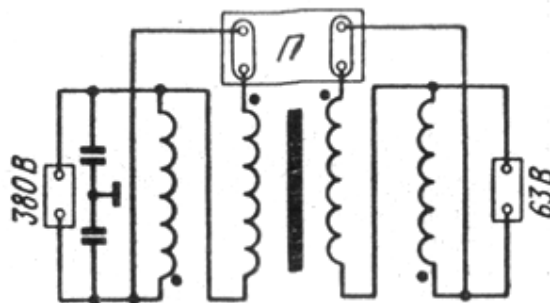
Электрическая схема сварочного трансформатора типа ТД-303;
